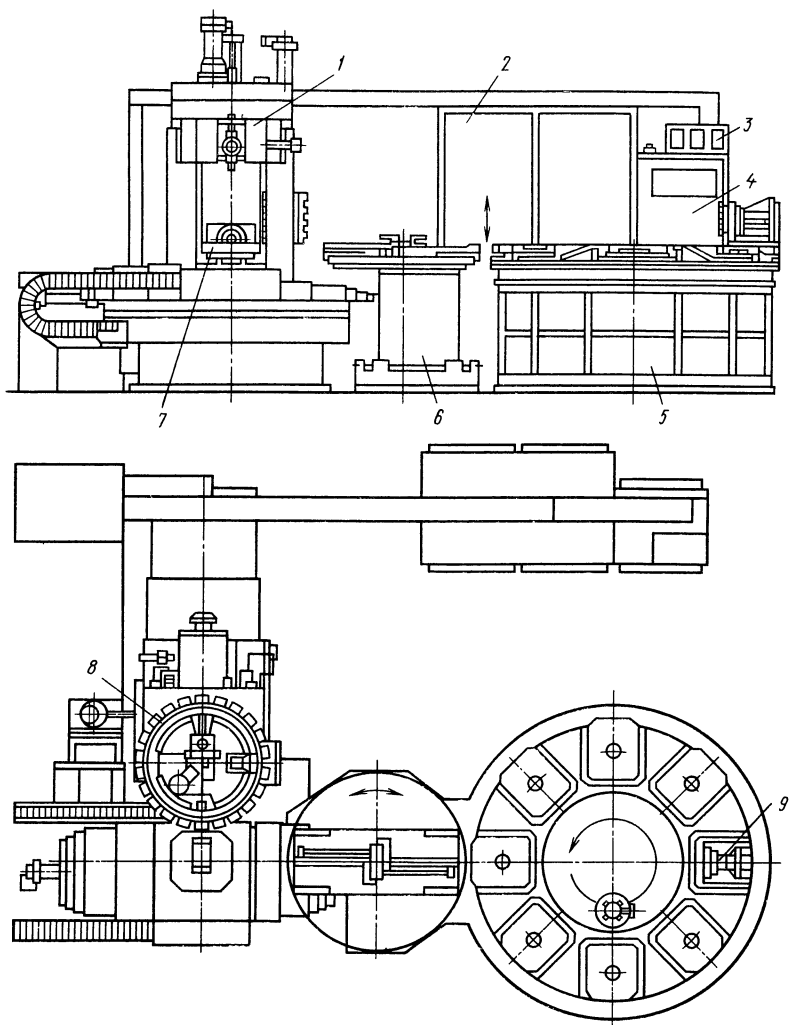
ГПМ для механической обработки корпусных деталей:
